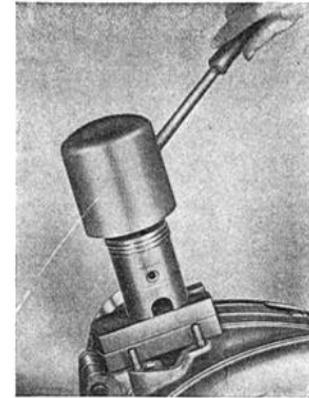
Anwärmen des Kolbens mittels Wärmekappe, die vorher im Schmiedeleuer oder mittels Schweißbrenner angewärmt wurde
